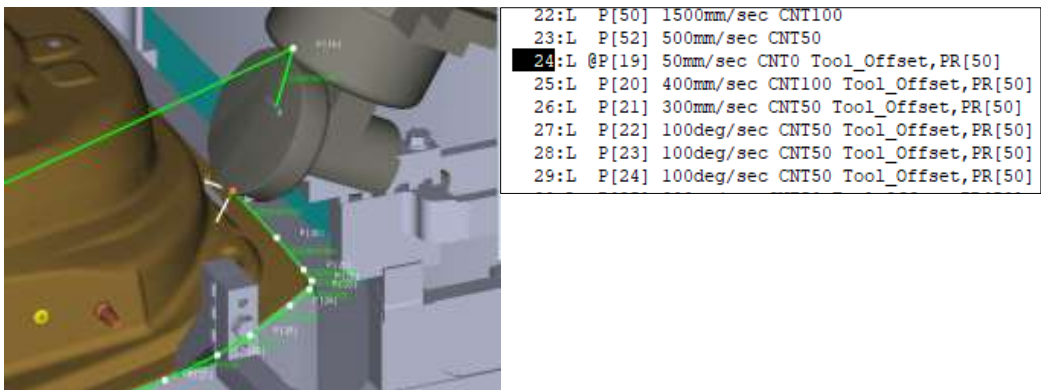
Robot C aproximación a la pieza para el engrapado de la esquina
